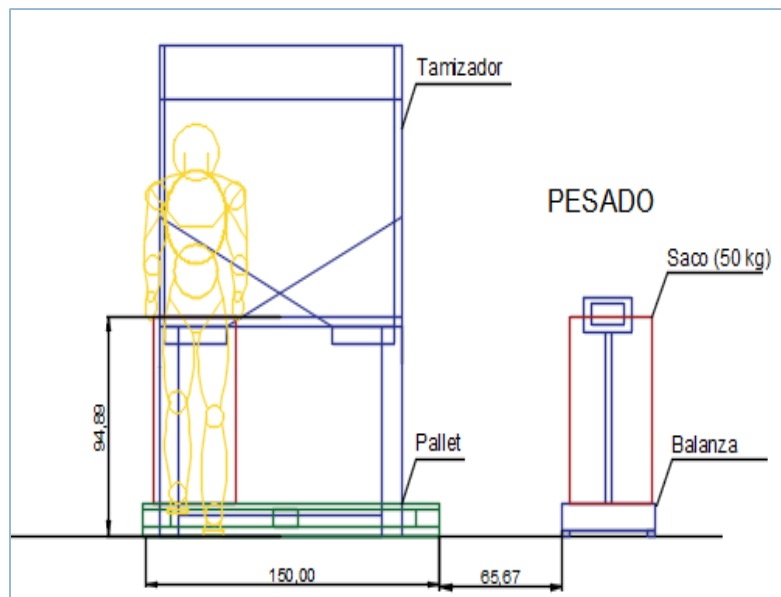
Puesto de trabajo de llenado y pesado – Vista frontal actual
